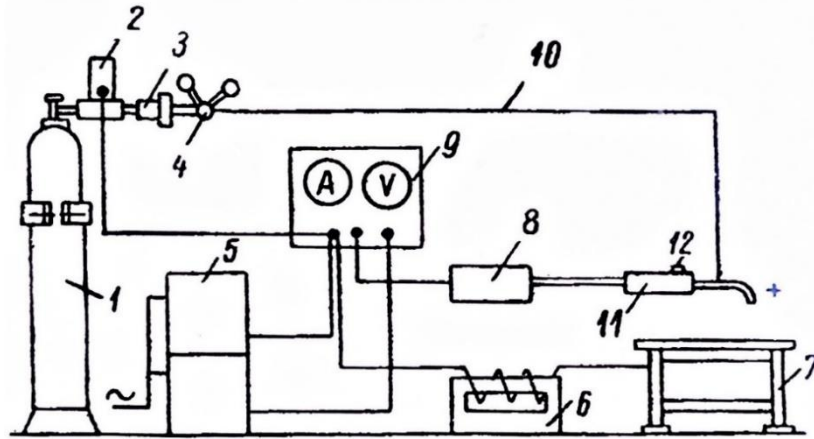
Схема установки для напівавтоматичного зварювання в середовищі вуглекислого газу: 1 – балон з вуглекислотою; 2 – перед-редукторний електричний підігрівник газу; 3 – осушувач газу; 4 – редуктор–витратомір; 5 – селенові випрямлячі ВСГ-3а; 6 – регулятор індуктивності (РСТЕ-24 або РСТЕ-34); 7 – стіл зварювальника; 8 – механізм подачі електродного дроту; 9 – пульт керування; 10 – шланг для подачі газу; 11 – газоелектричний пальник; 12 – кнопка включення
